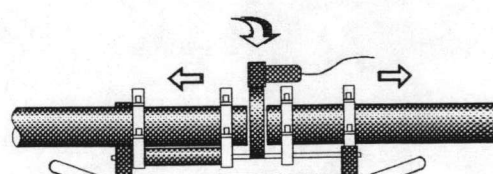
แสดงแผนภูมิกระบวนการเชื่อมต่อท่อ แบบ BUTT-FUSION WELDING
